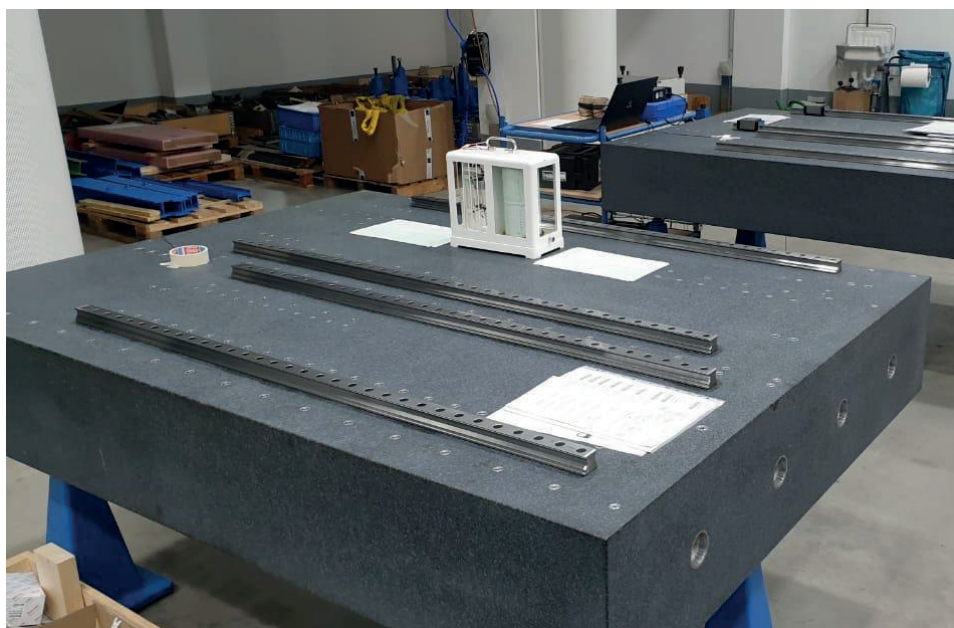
Гранитная станина высокоточного токарного обрабатывающего центра модели «ТМ – 160»
